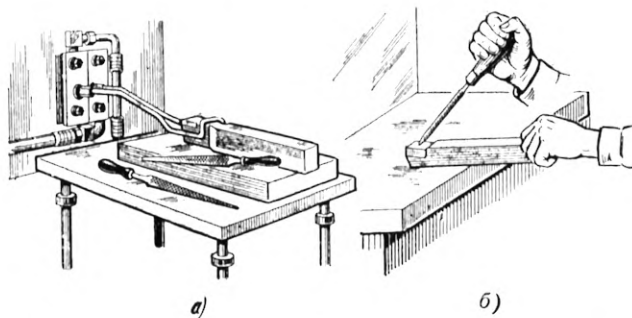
Напайка твердосплавной пластины на державку резца токами высокой частоты:
